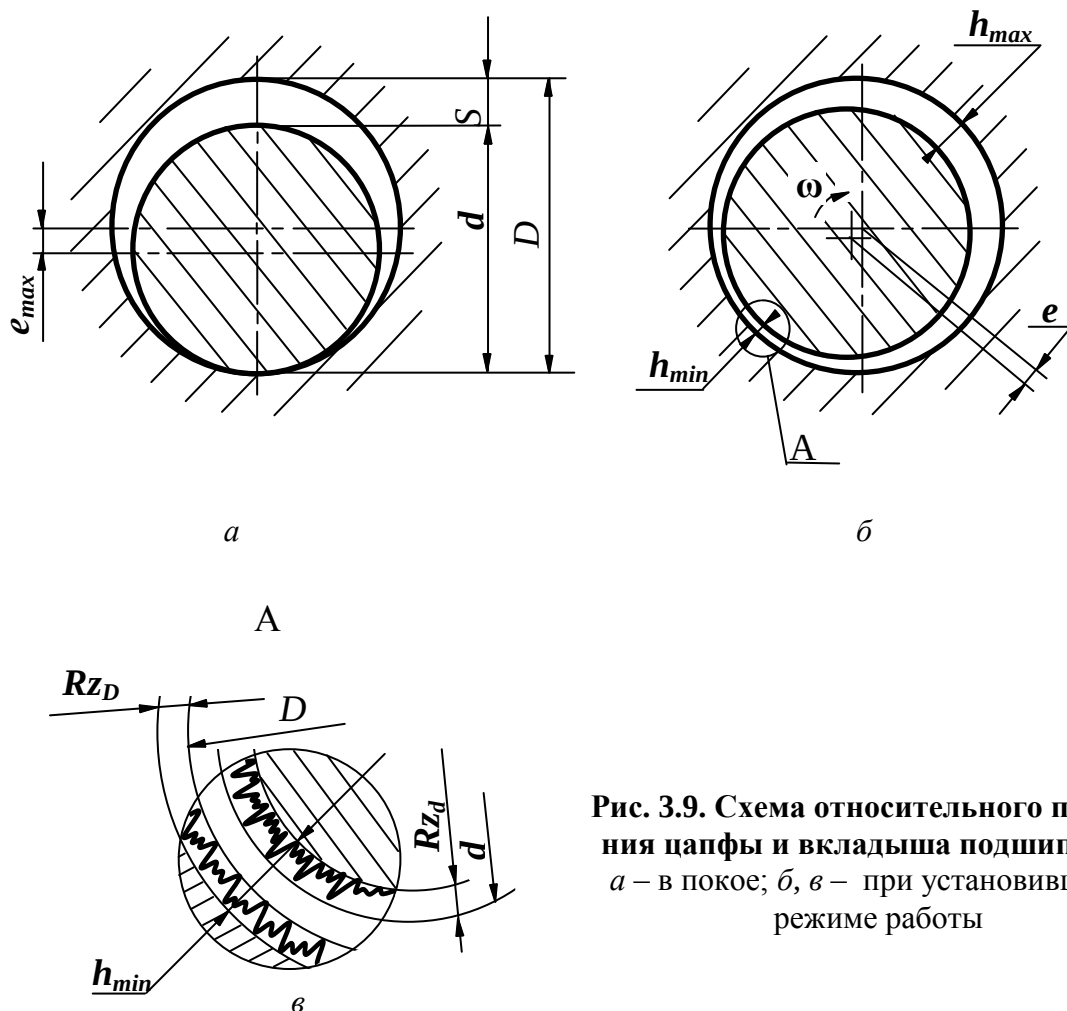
Схема относительного положения цапфы и вкладыша подшипника:
